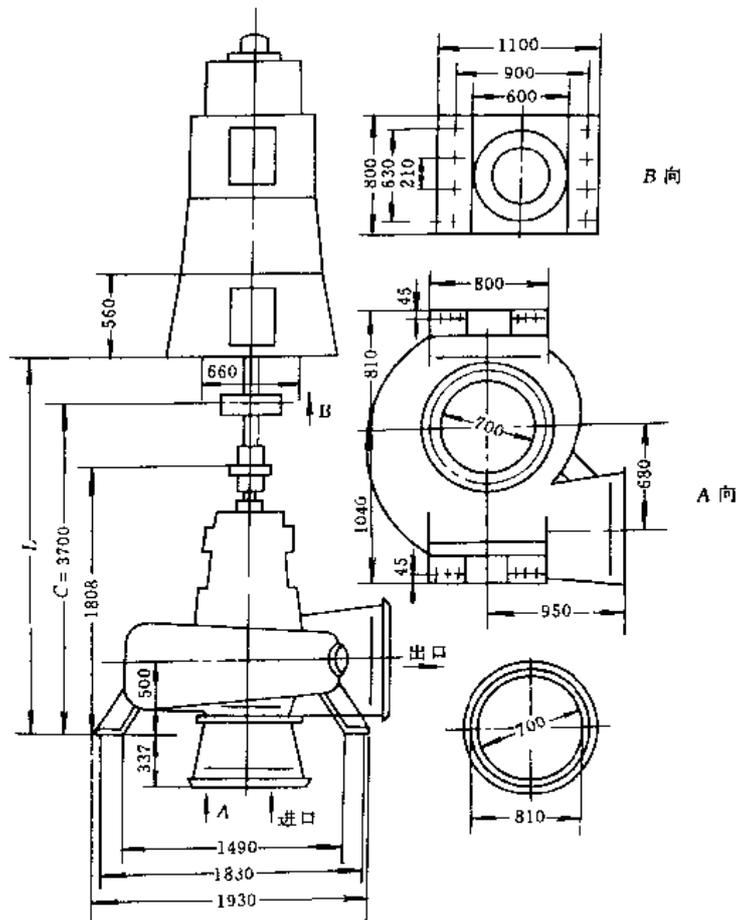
700HLWB—10 型泵外形尺寸 (单位: mm)
